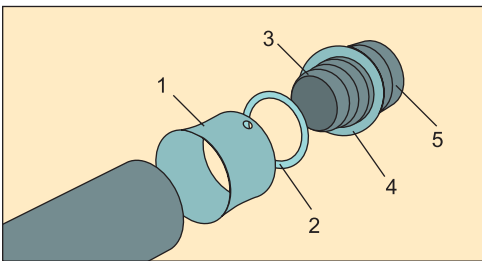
Пресс-фитинг: 1 — обжимная гильза; 2 — пластиковое диэлектрическое кольцо; 3 — уплотнительные кольца; 4 — фиксатор гильзы; 5 — корпус
